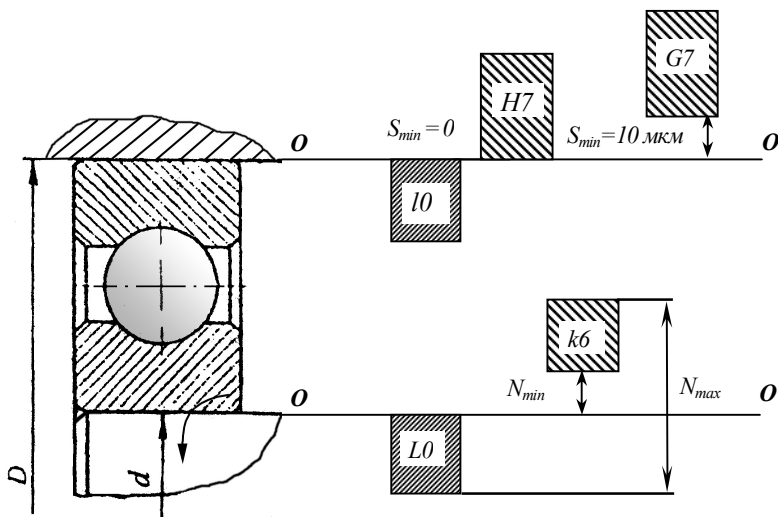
Схемы полей допусков для соединений подшипника качения с валом и корпусом
